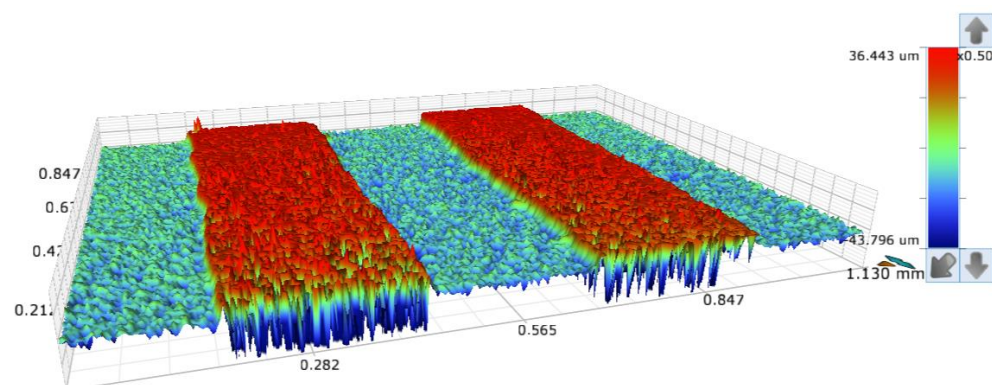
Mesure des dimensions des pistes de la bobine en 3D au profilomètre.
